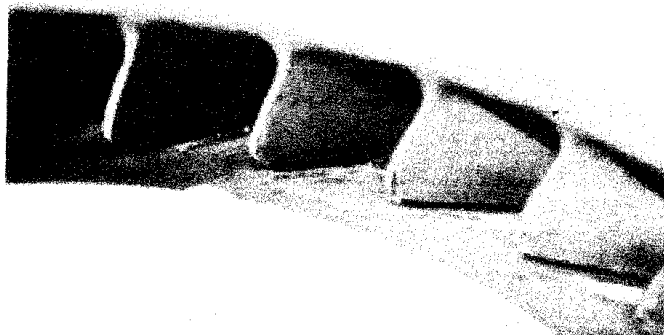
Ерозійний знос лопаток колеса 1-ї ступені ротора
